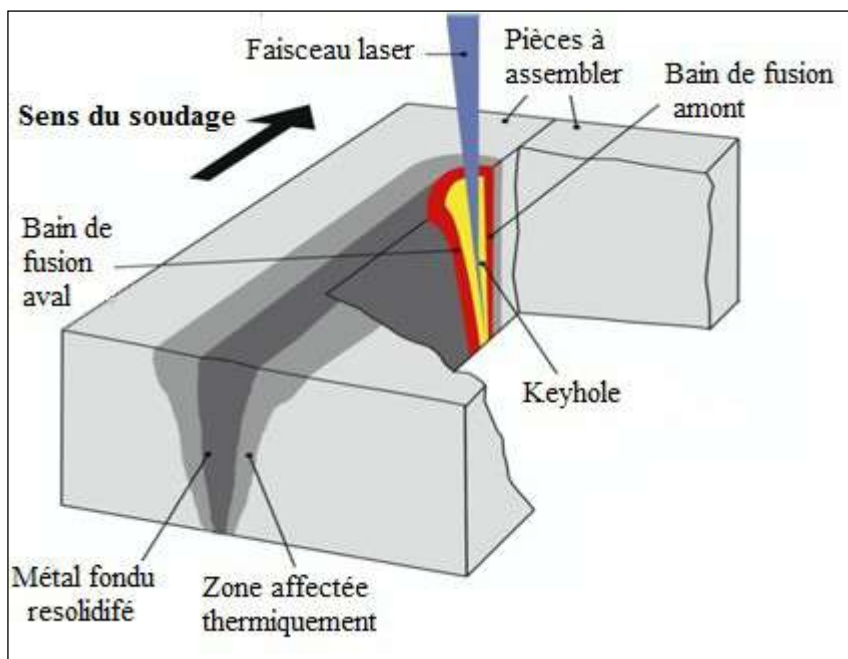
Principe de soudage métallique par laser [47]
